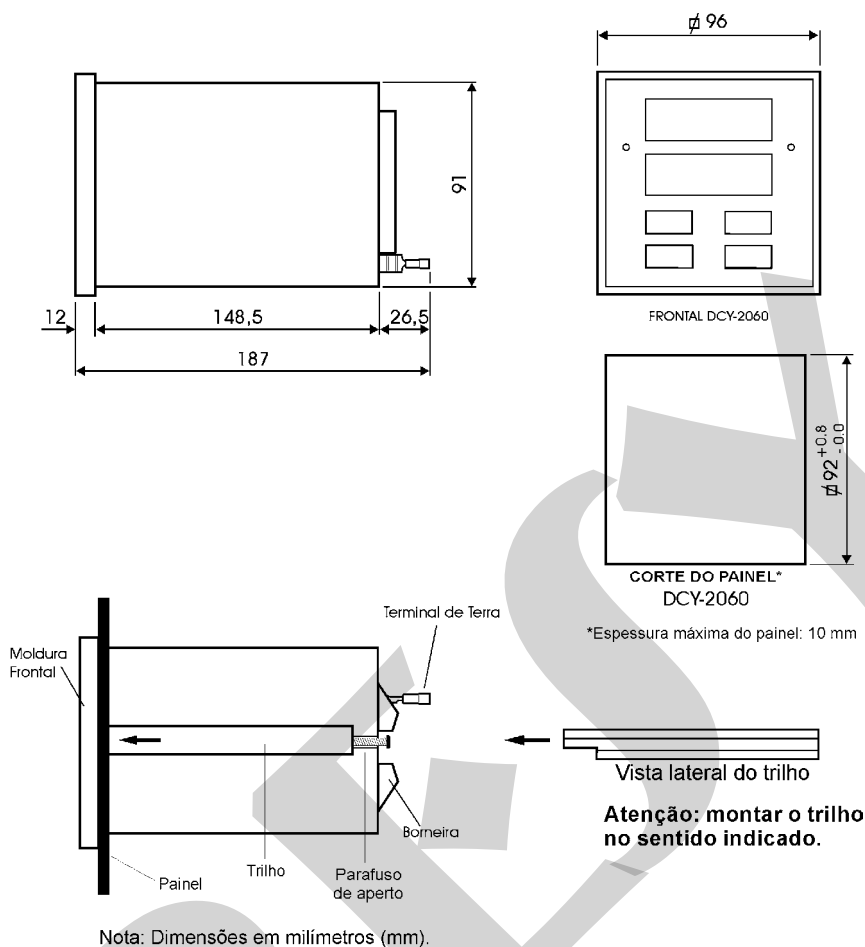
Desenho dimensional, corte e vista lateral da montagem no painel do controlador DCY-2060.
